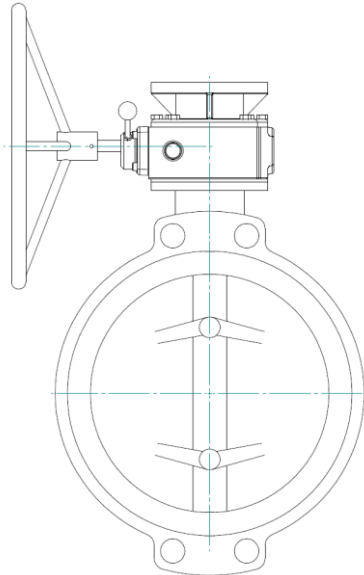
Reductor en posición perpendicular y en la parte superior de la válvula
